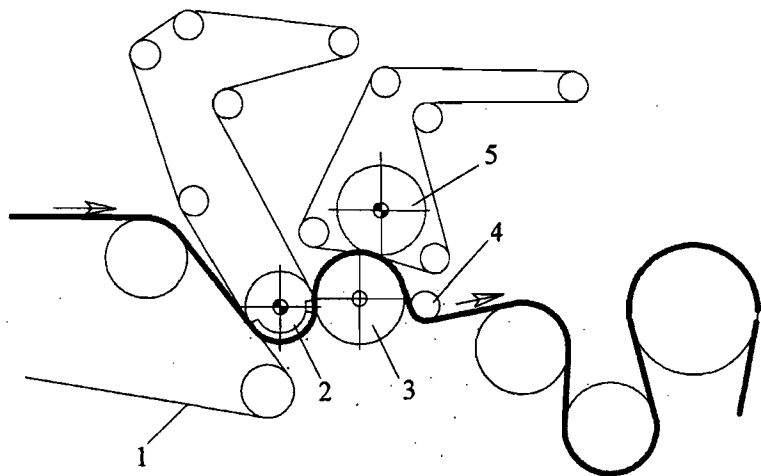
Combi пресс: 1 – сетка; 2 – отсасывающий вал; 3 – гранитный вал; 4 бумаговедущий валик; 5 – желобчатый вал
